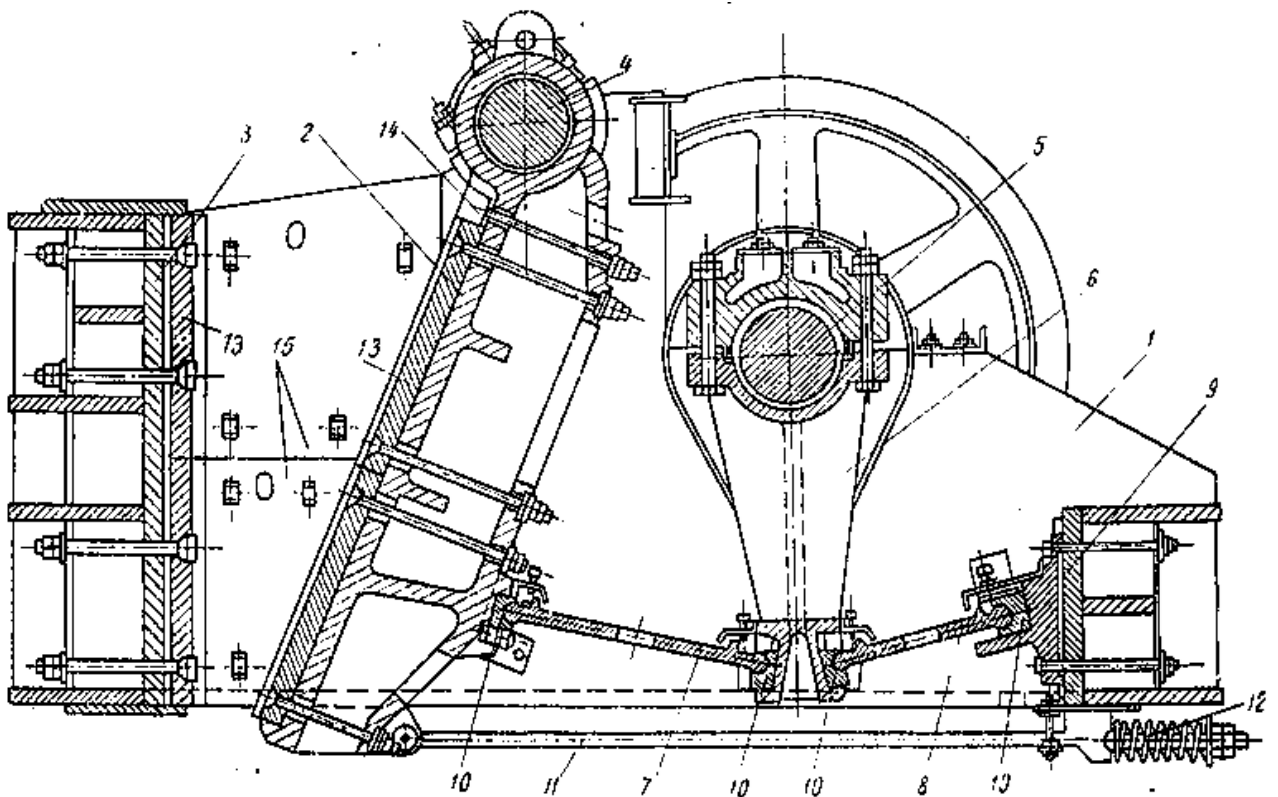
Щековая дробилка с простым движением щеки [60]
